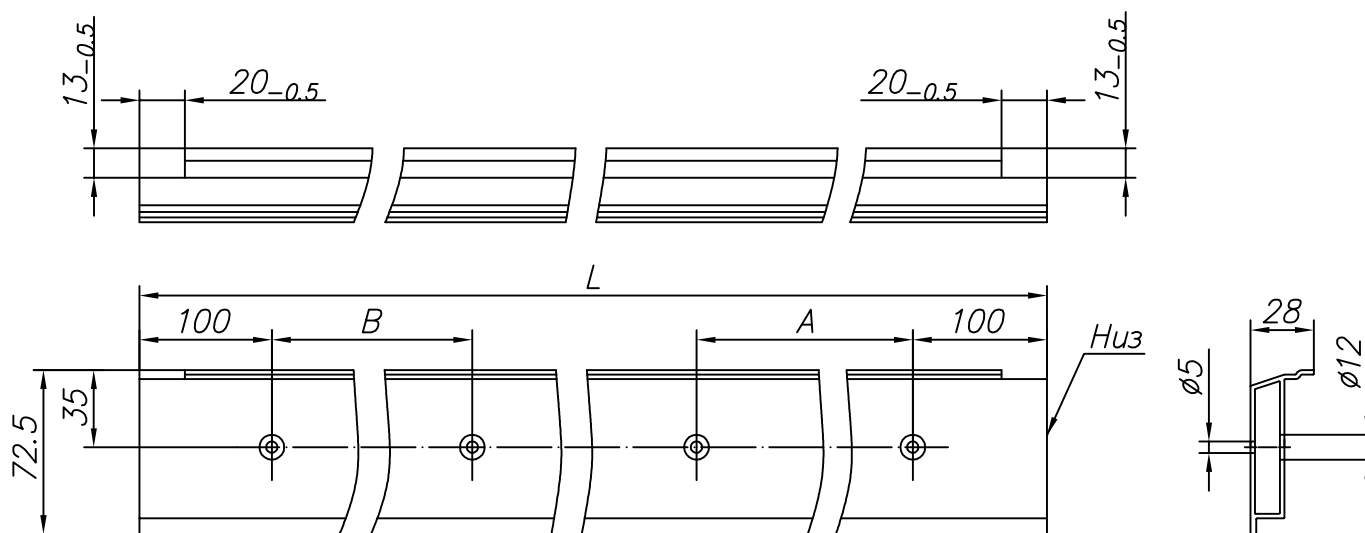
Изготовление притвора без паза для ответной пластины замка из профиля FLGU.400.0505 (открытие внутрь)
